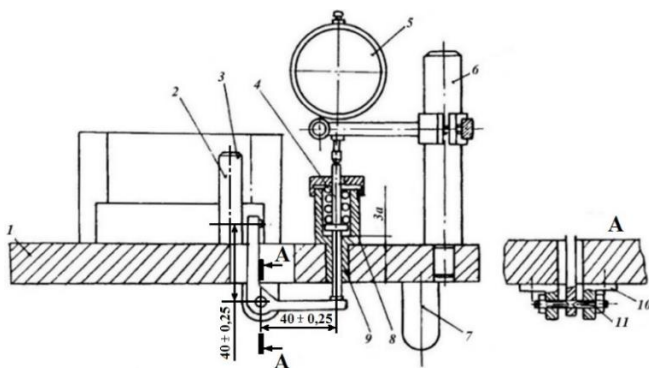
Контрольное приспособление для проверки радиального биения внутренних цилиндрических поверхностей
